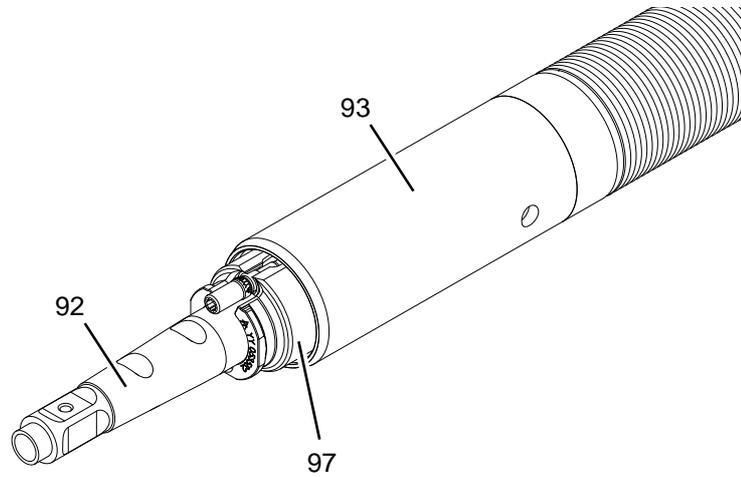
Faire glisser le carter de serrage sur le burin
